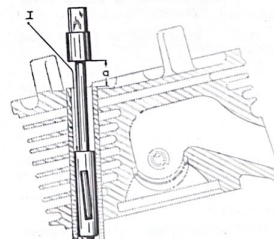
Utilización del aparato 3005 - T para el engrase de los tubos protectores de las varillas de balancines.
